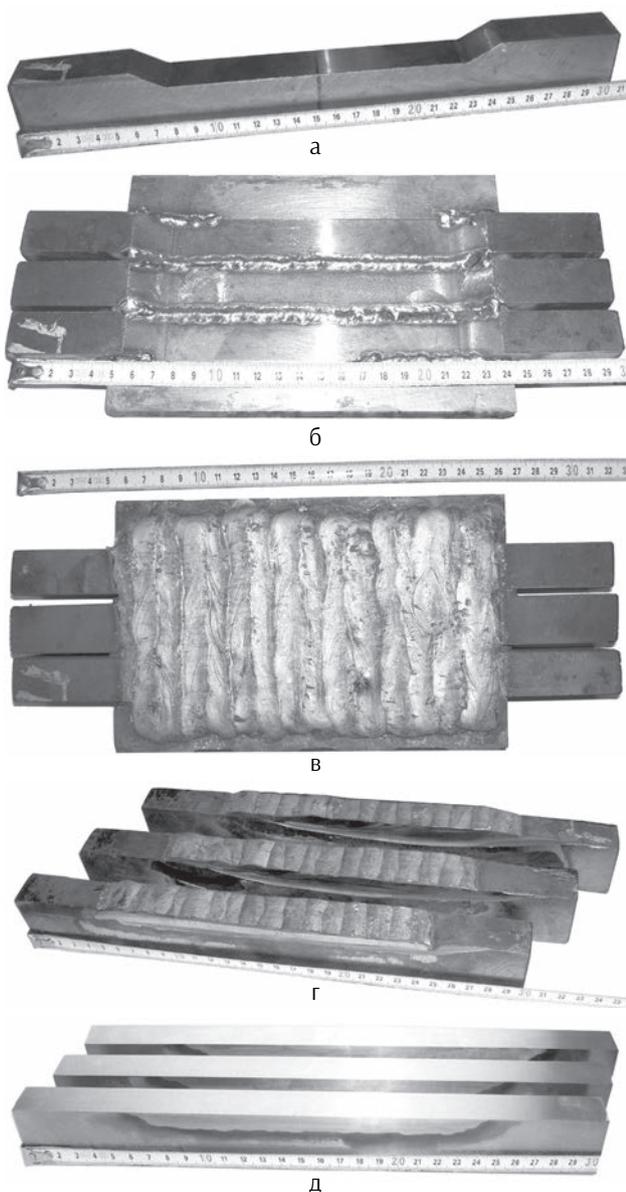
Этапы изготовления наплавленных образцов: заготовка с разделкой под наплавку (а); заготовки, собранные в пакет (б), после наплавки (в), порезки (г) и финишного шлифования (д)
